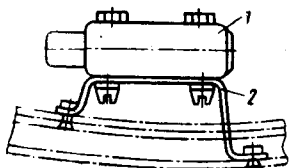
Типовое крепление готового изделия болтами по анкерным гайкам:
